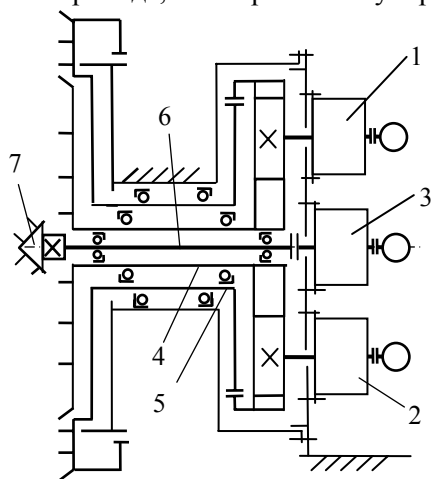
Кинематическая схема привода соосных буров исполнительного органа со спаренными планетарными редукторами и приводом активного забурника
